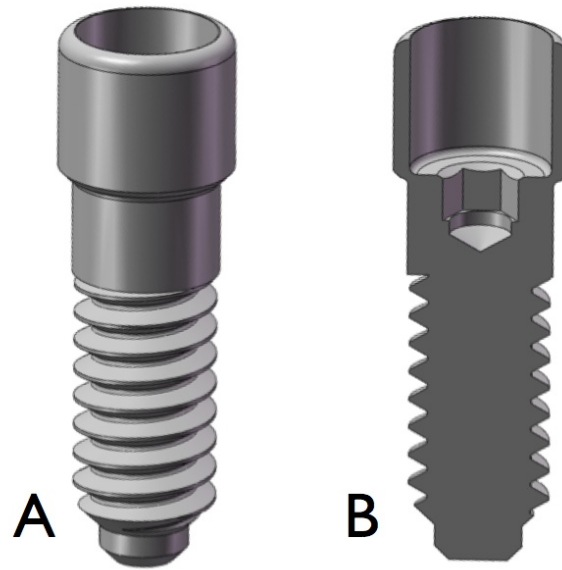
Diseño gráfico del tornillo prototipo 1. (A) Visión lateral. (B) Corte seccional en el que se aprecia la posición del hexágono del destornillador situada en el cuerpo del tornillo.
